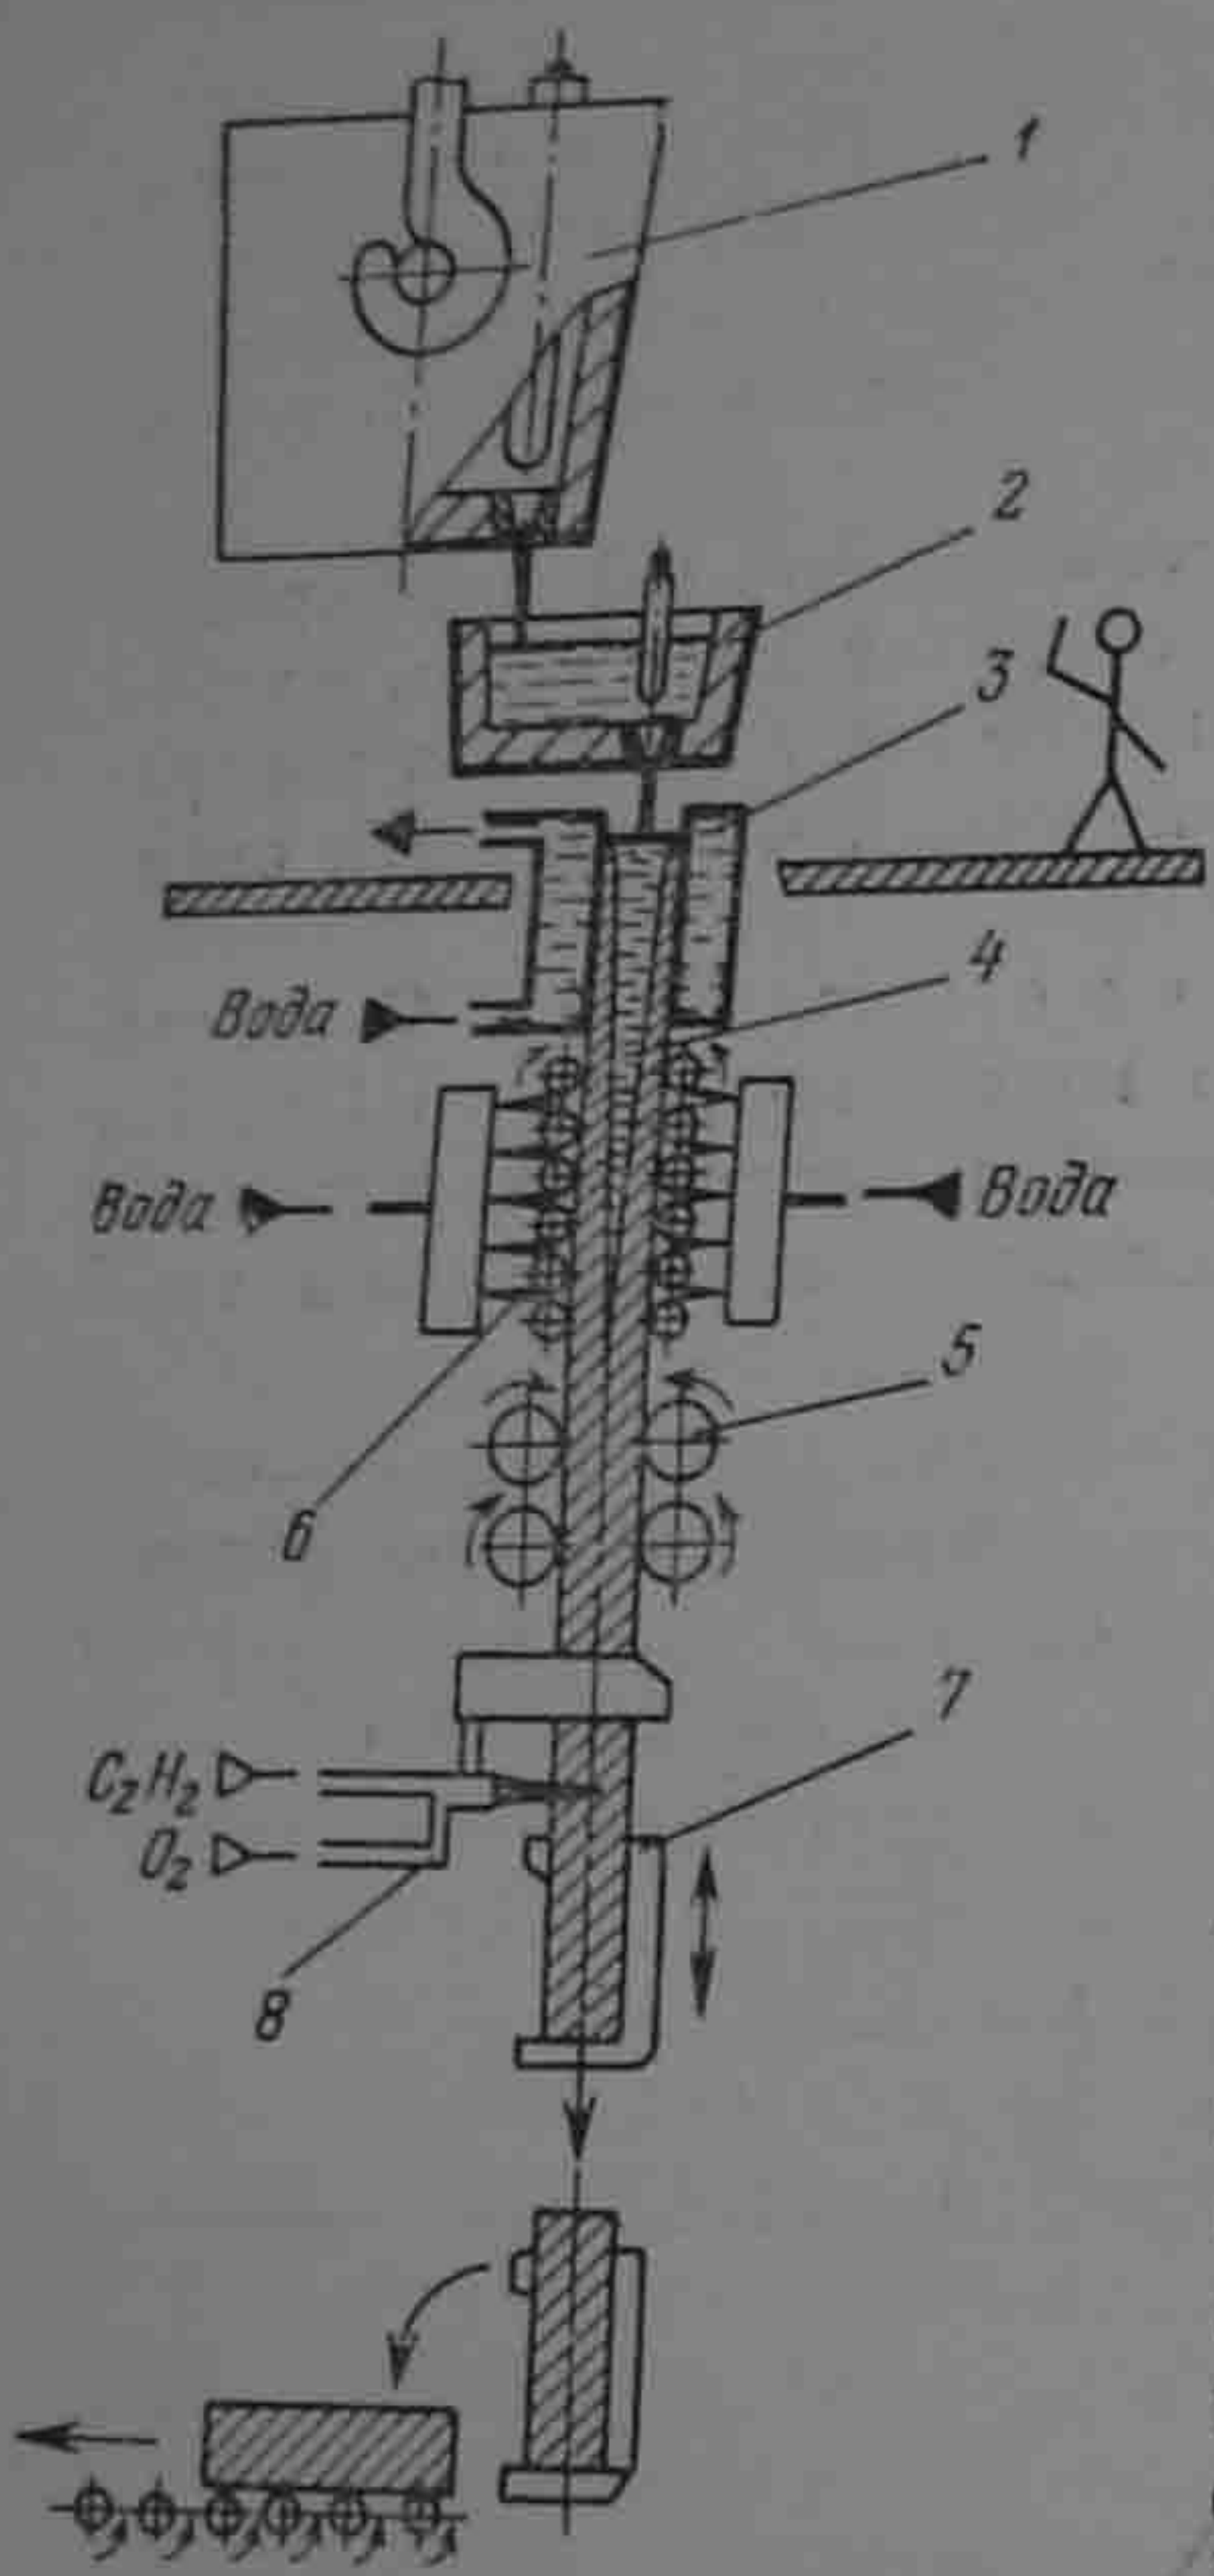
Схема установки для непрерывной разливки стали (УНРС)
